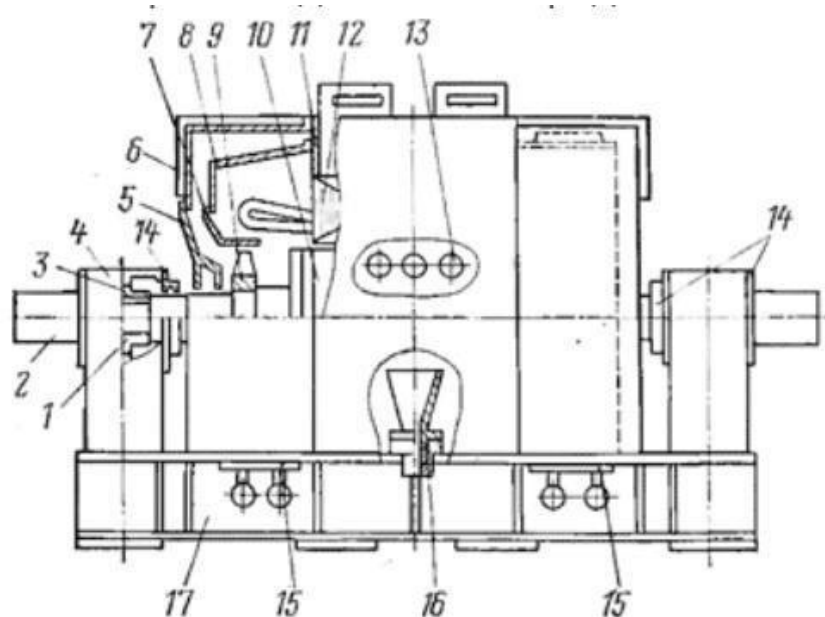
Двигун 2АЗМ 5000/6000: 1 - нижній вкладиш підшипника, 2 - вал, 3 - верхній вкладиш підшипника, 4 - кришка підшипника; 5 - повітрянаправляючий зовнішній щит, 6 – кожух, 7 – дифузор, 8 - повітрянаправляючий внутрішній щит, 9 – вентилятор, 10 - сердечник ротора, 11 - корпус статора, 12 сердечник статора, 13 - ізолятори ввідного пристрою, 14 - лабіринтові ущільнення, 15 – повітроохолоджувач, 16 - ввідний пристрій, 17- монтажна плита
